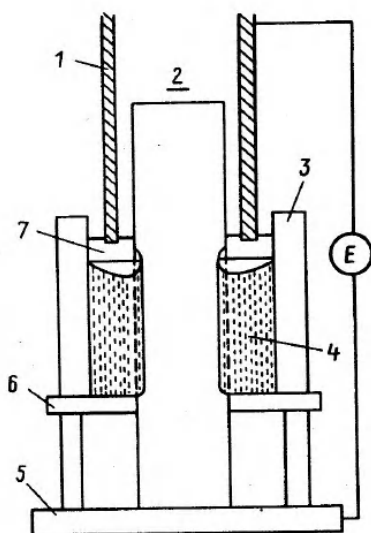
Схема установки для электрошлаковой наплавки: 1 - электрод; 2 - сердечник; 3 - кристаллизатор; 4 - наплавленный слой; 5 - поддон; 6 - заправка; 7 - шлаковая ванна
